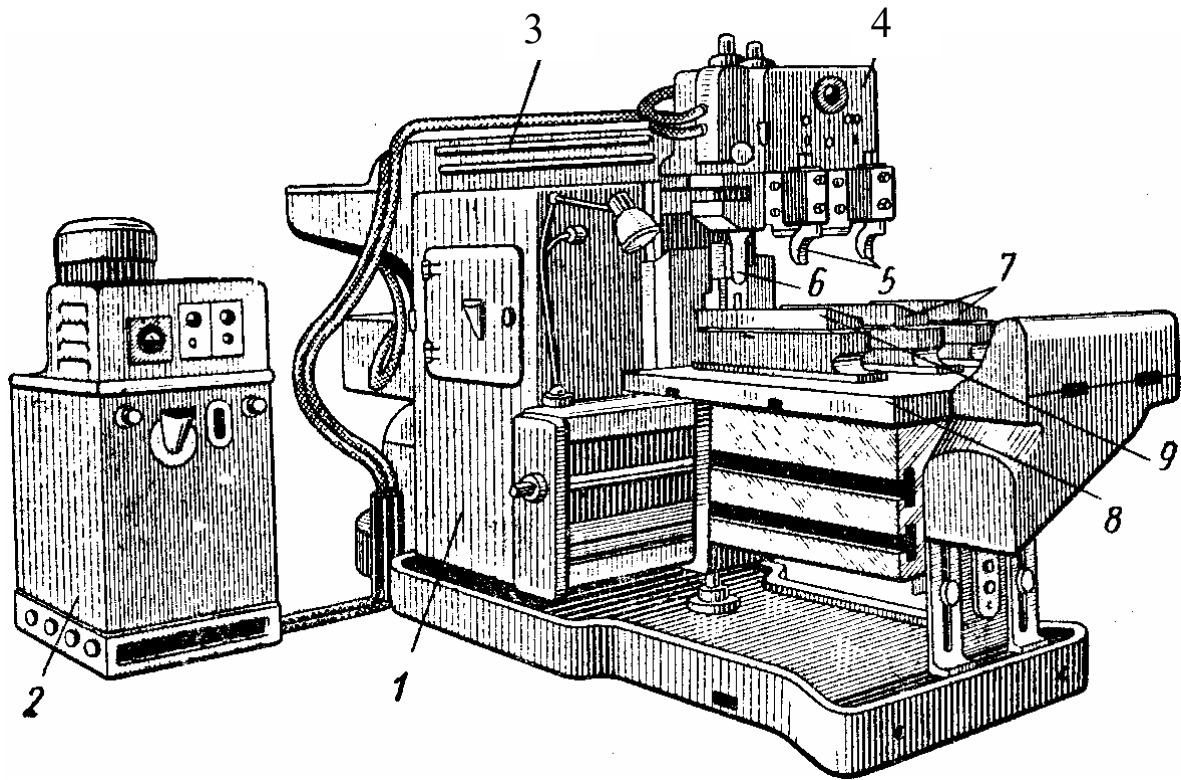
Гідрокопіювальний поперечно-стругальний верстат мод. ГД-21: 1 – станина; 2 – гідростанція; 3 – консоль; 4 – копіювальний супорт; 5 – різці; 6 – копіювальний щуп; 7 – заготовка; 8 – стіл; 9 - копій
